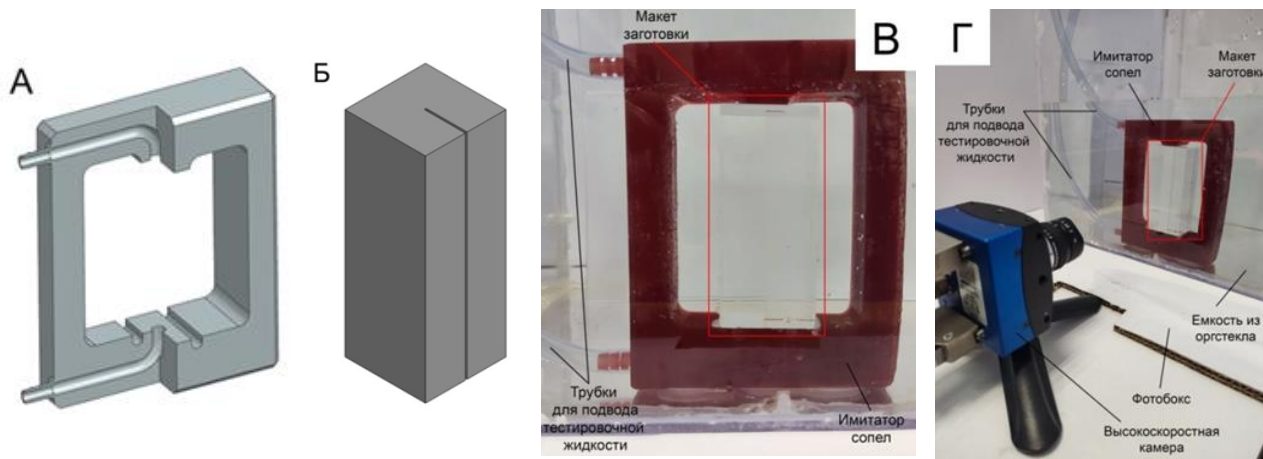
Стенд для проведения высокоскоростной съемки потоков тестировочной жидкости при прокачке через рабочую зону макета заготовки: а – имитатор сопел станка Sodick VZ300L; б – 3D-модель макета заготовки; в – имитатор сопел с установленным макетом заготовки из оргстекла; г – общий вид стенда – взаимное расположение емкости из оргстекла, имитатора сопел, фотобокса, макета заготовки и высокоскоростной видеокамеры
